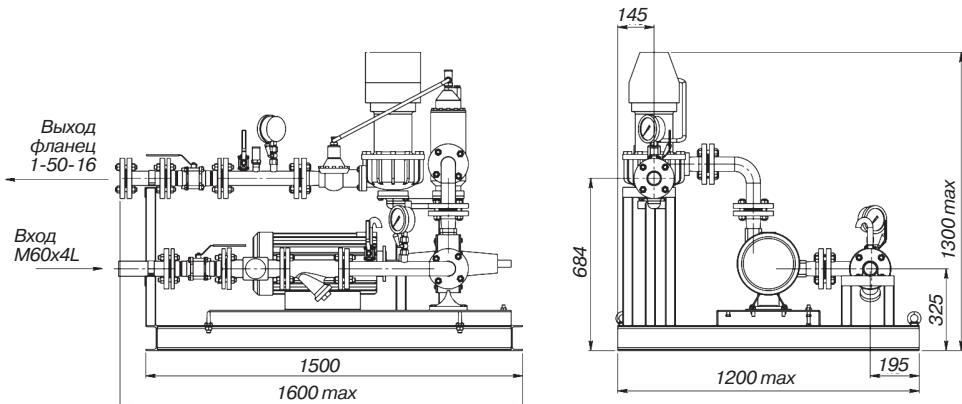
Габаритно-присоединительный чертеж установки насосно-счетной Vortex
